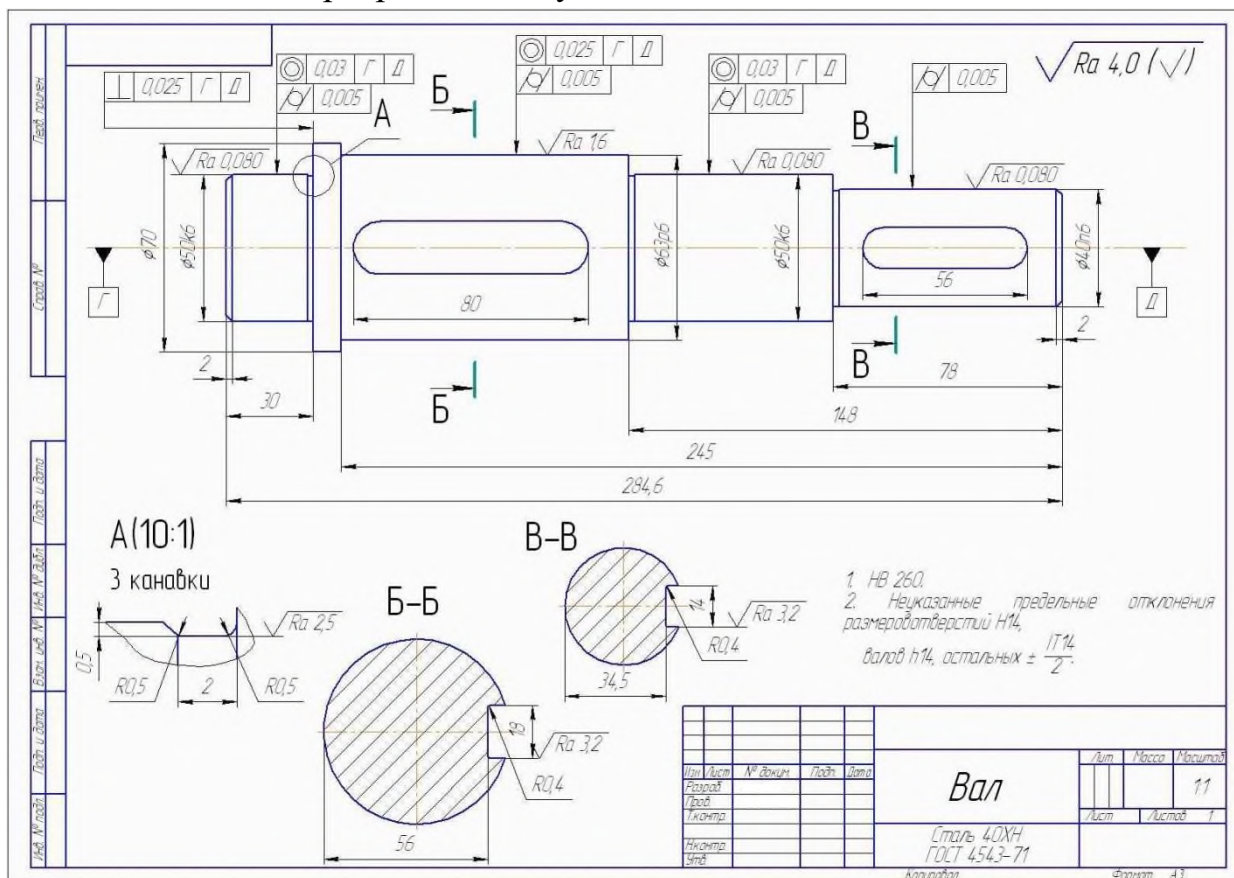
Рабочий чертеж ведущего вала цилиндрического редуктора
